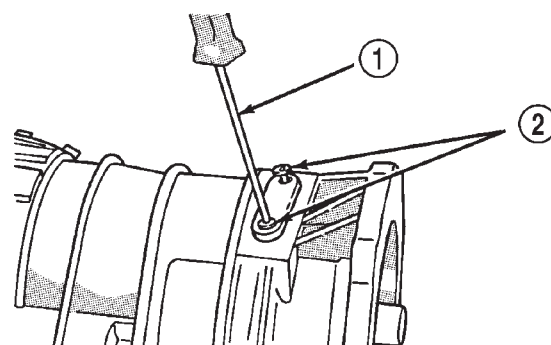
Desmontaje e instalación del tornillo de la tapa de acceso
